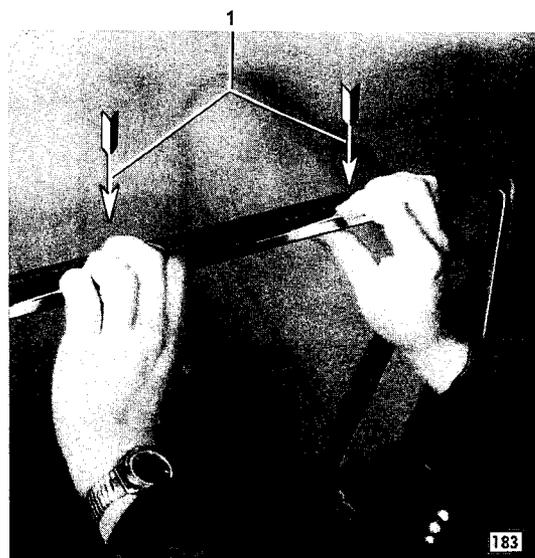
Dichtung auf Türklebeflächen fest aufdrücken
